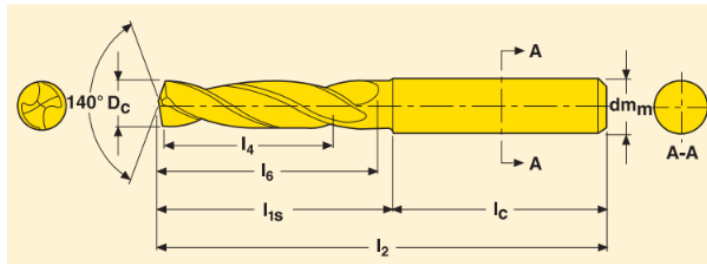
Свердло SD1103-0680-024-08R1 [14, с.26]
